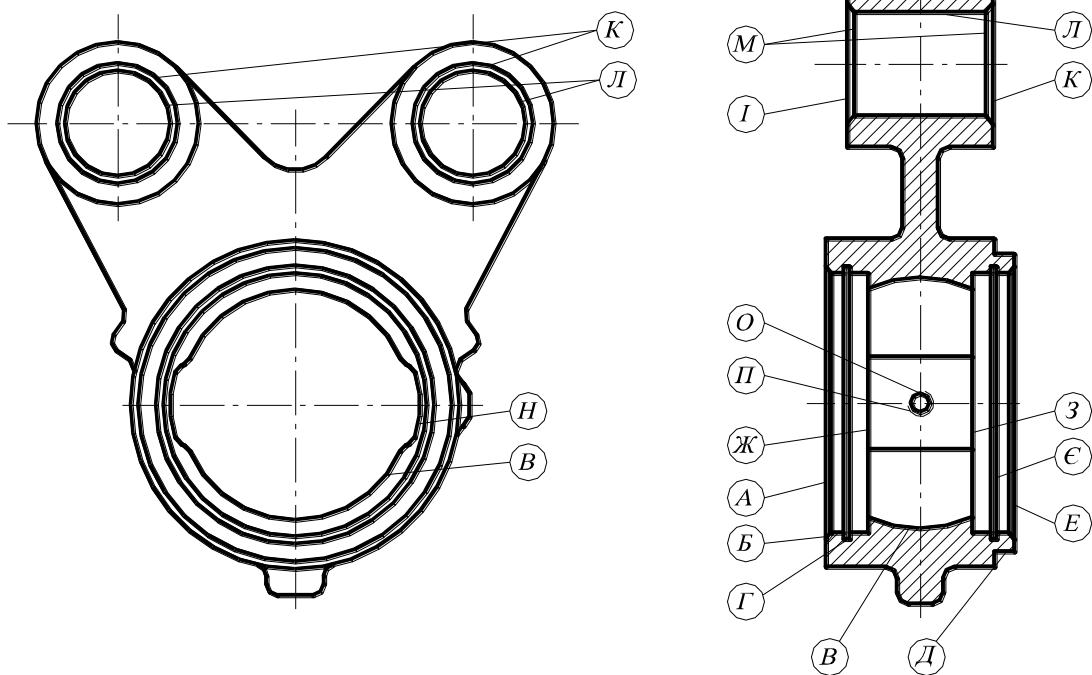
Ескіз деталі Корпус ОГ 1-45.314
